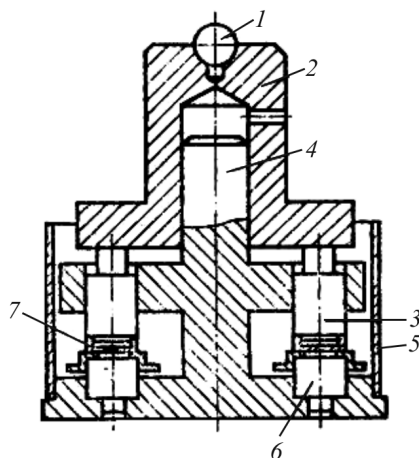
Типовая конструкция простейшего многоместного приспособления для диффузионной сварки: 1 – шарик; 2 – прижим; 3 – пуансон; 4 – корпус; 5 – тепловой экран; 6 – центрирующая оправка; 7 – свариваемые детали
